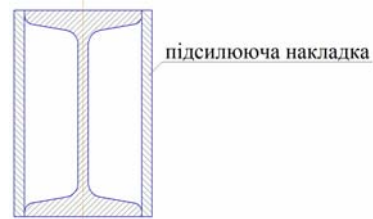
Переріз основної повздовжньої балки рами вагона-платформи зчленованого типу
